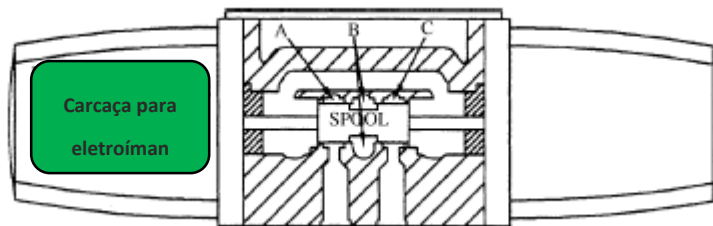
Válvula Solenóide (Die Cast Engineering [6])
